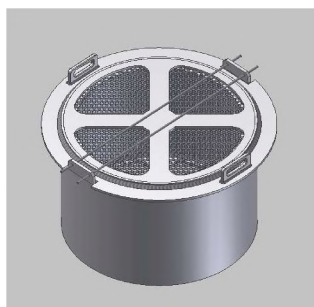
3D-модель корпуса сорбционного фильтра
